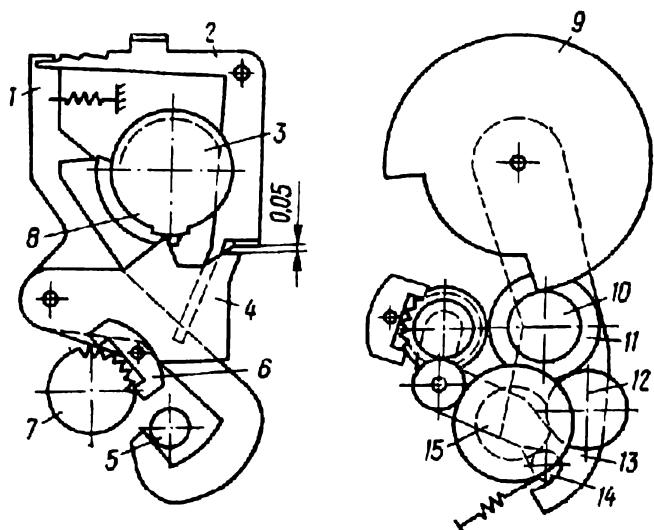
Положение деталей тормозного механизма на выдержке «В»:
